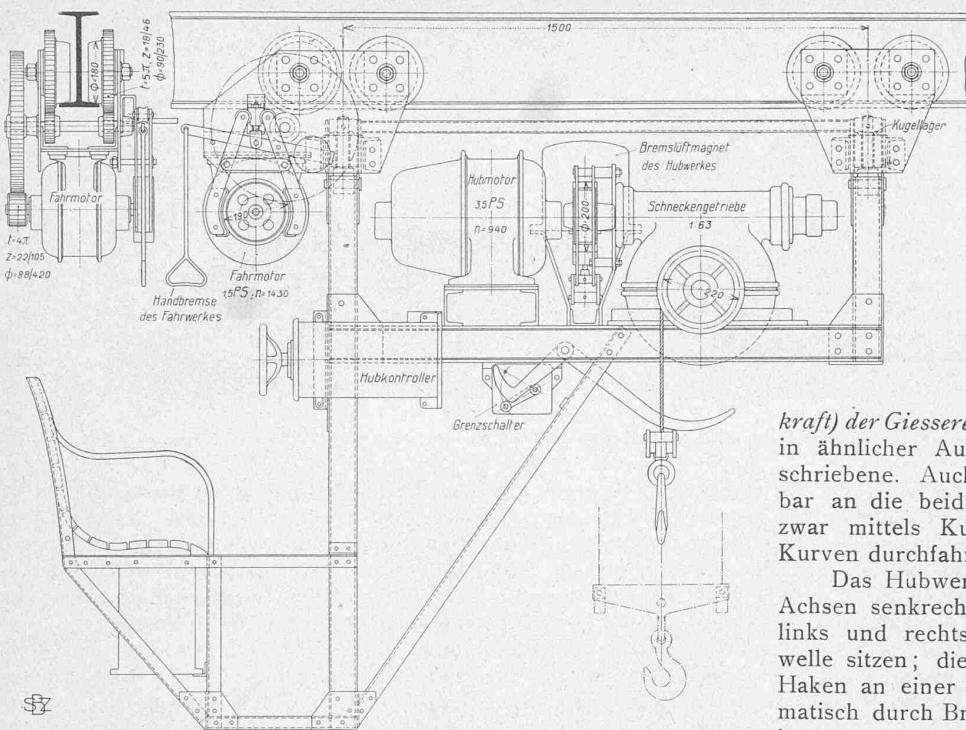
Motor-Laufwinde für 1000 kg. — Giesserei Bern. — 1:20.
